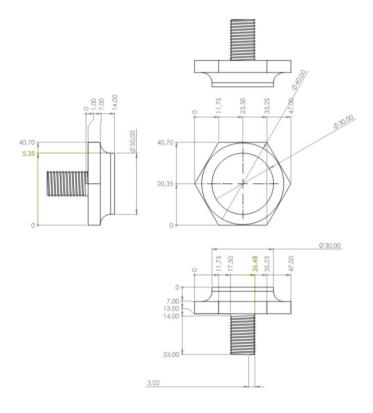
Mise en plan du pied sur SolidWorks.
